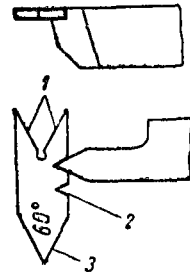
Шаблон для контроля профиля и правильности установки резьбовых резцов.
